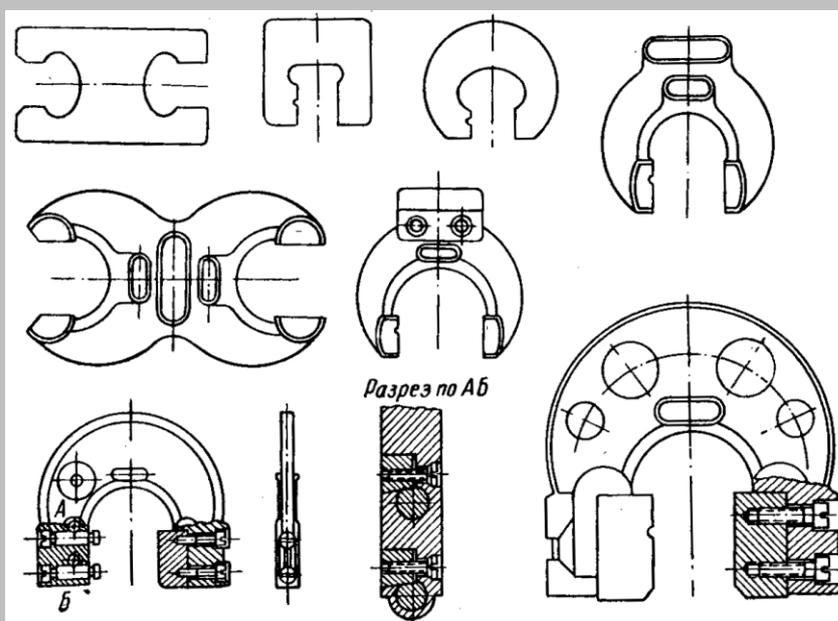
Гладкие калибры-скобы и их конструкции
